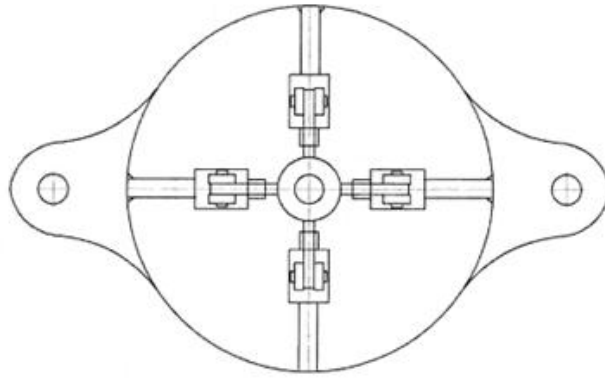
б - Опора силового агрегата с регулируемой характеристикой (вид сверху)
